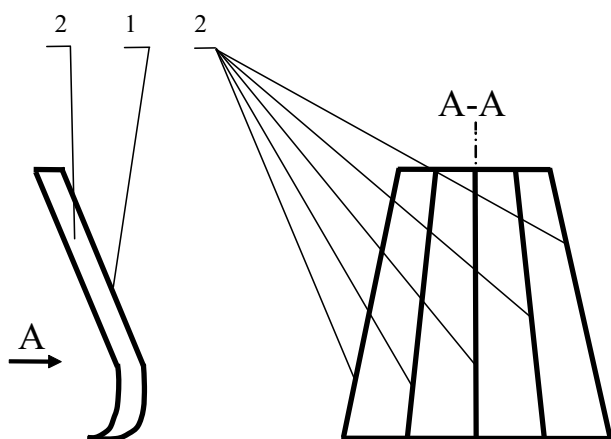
Конструкция делителя зерновой дробилки КДУ-2:
